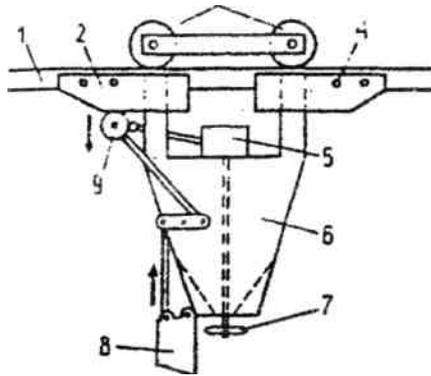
Устройство для раздачи корма в рыбноводных бассейнах. 1 - направляющая; 2 - копиры; 3 - ролики; 4 - зажимы; 5 - редуктор; 6 - бункер; 7 - пропеллерный разбрасыватель; 8 - щиток; 9 - приводной ролик.
